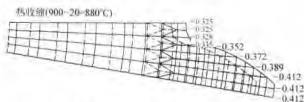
温锻圆锥齿轮齿形的热收缩
